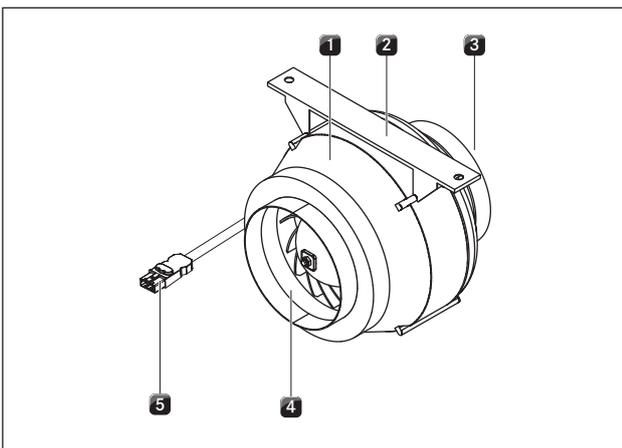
Aufbau Ergänzungsrohrlüfter
